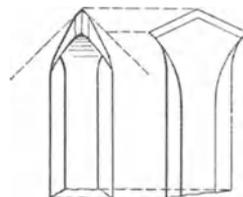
Zuschärfung des Bohrmeißels bei einem Meißelbohrer.
